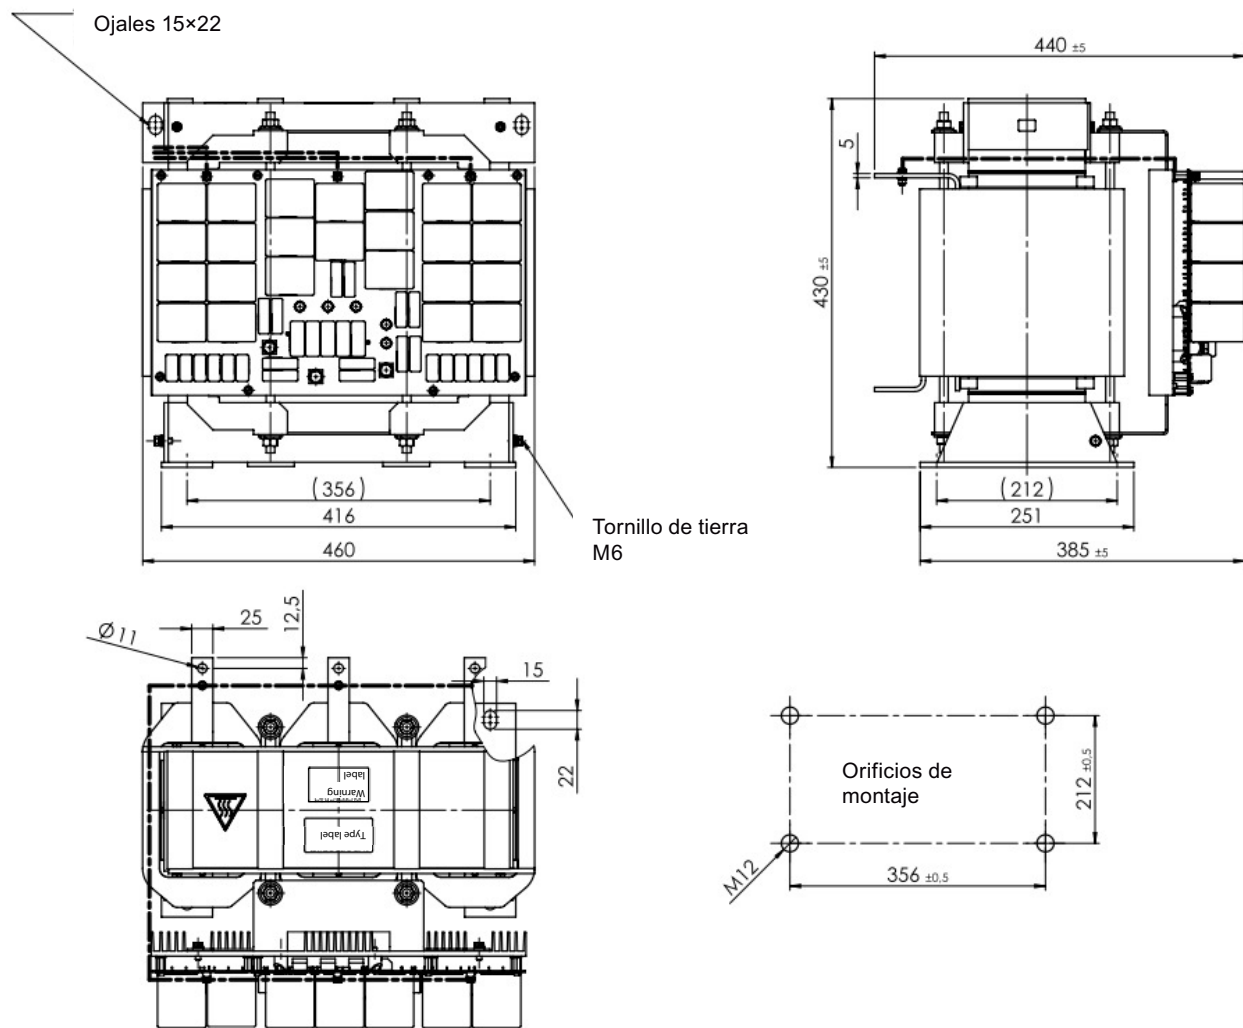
Dimensiones de JTA:TEF1203-0MB
